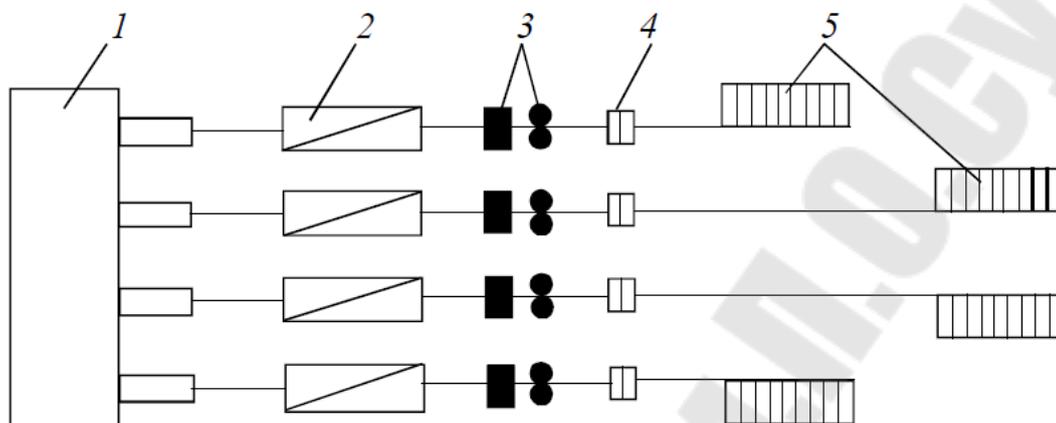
Схема расположения оборудования заготовочного литейно-прокатного агрегата:
